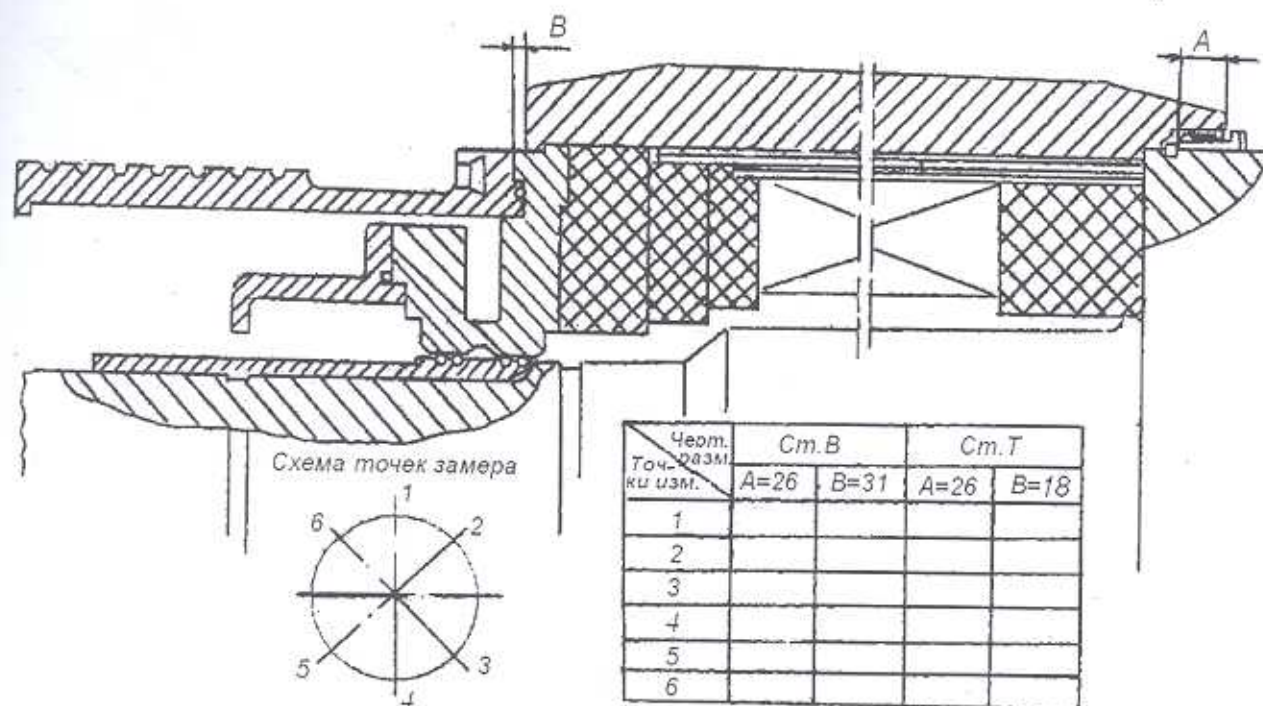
Формуляр сборки бандажных колец и узлов водоподвода
